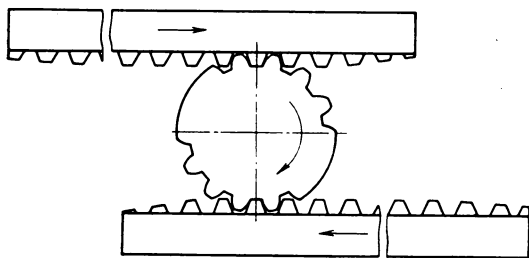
Схема накатывания зубьев вала плоскими рейками
